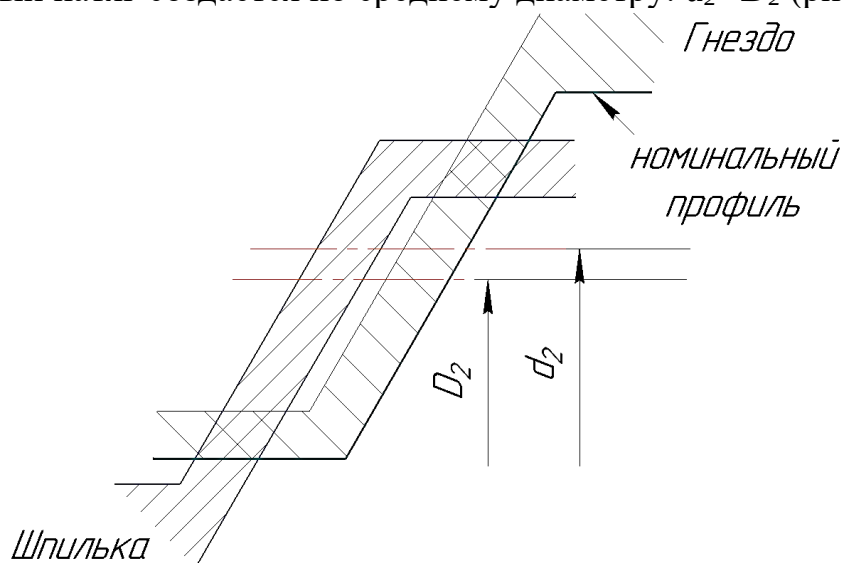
Схема полей допусков резьбы с натягом
